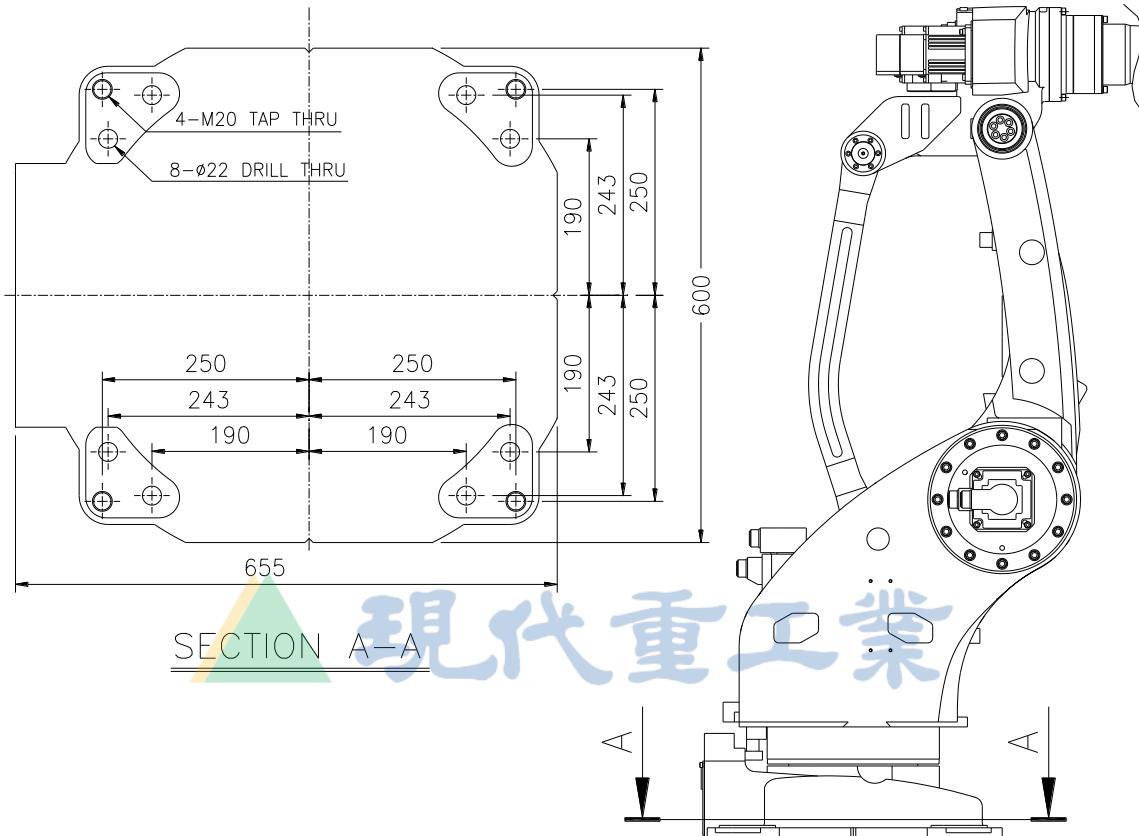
机器人安装面尺寸 : [HR050/HR030L]
